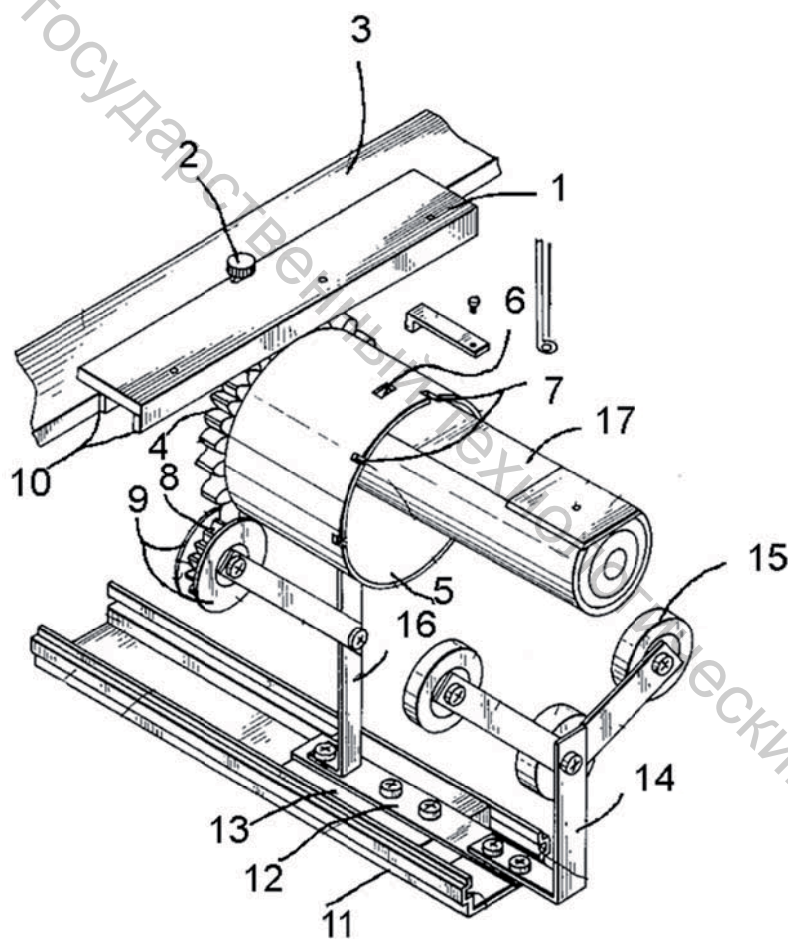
Каретка координатного устройства с приспособлением для вышивки на готовых изделиях
